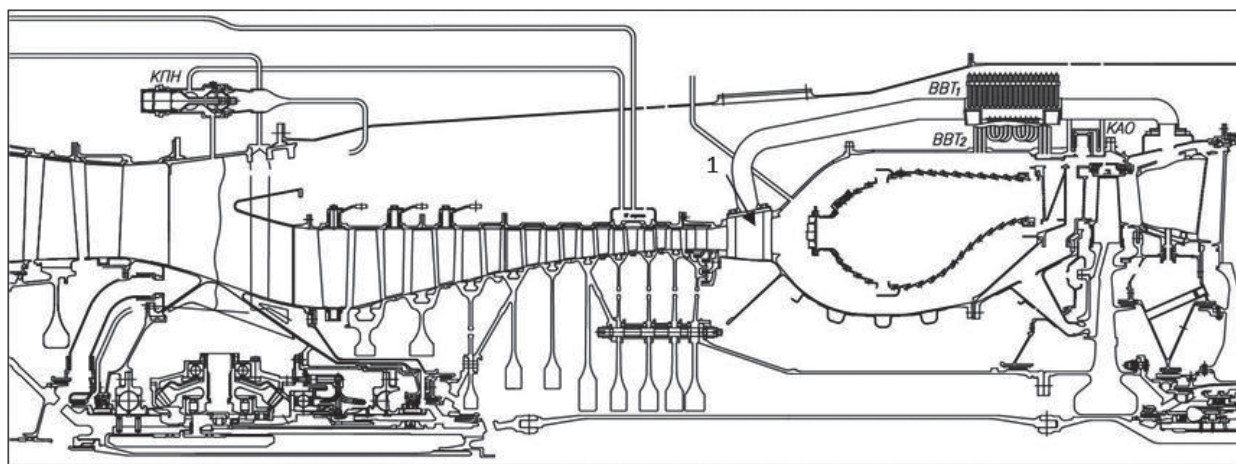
Конструктивная схема воздушной системы двигателя прототипа
